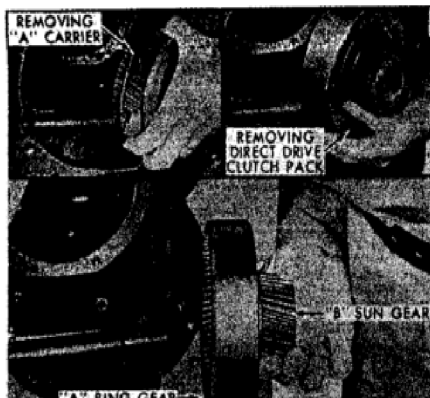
Verwijderen "B" Zon- "A" Ring Gear, "A" Carrier en Direct Drive Clutch als-semblies.
